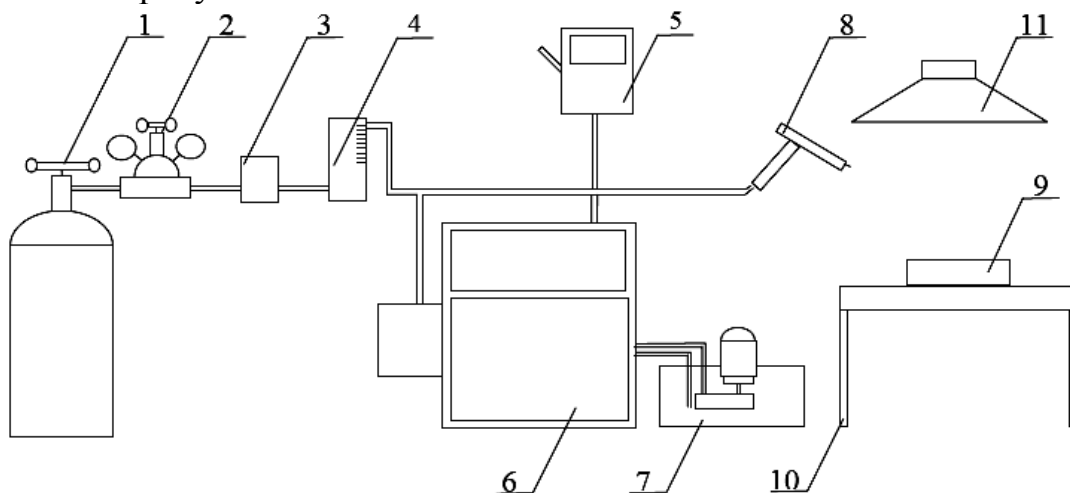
Схема рабочего поста для аргонодуговой сварки: 1-баллон с аргоном; 2 – газовый редуктор; 3 - электропневмоклапан; 4 – ротаметр; 5- шкаф электропитания; 6 – установка для аргонодуговой сварки; 7 – станция охлаждения; 8 – горелка; 9 – свариваемое изделие; 10 – рабочий стол; 11 – вытяжной зонт.
